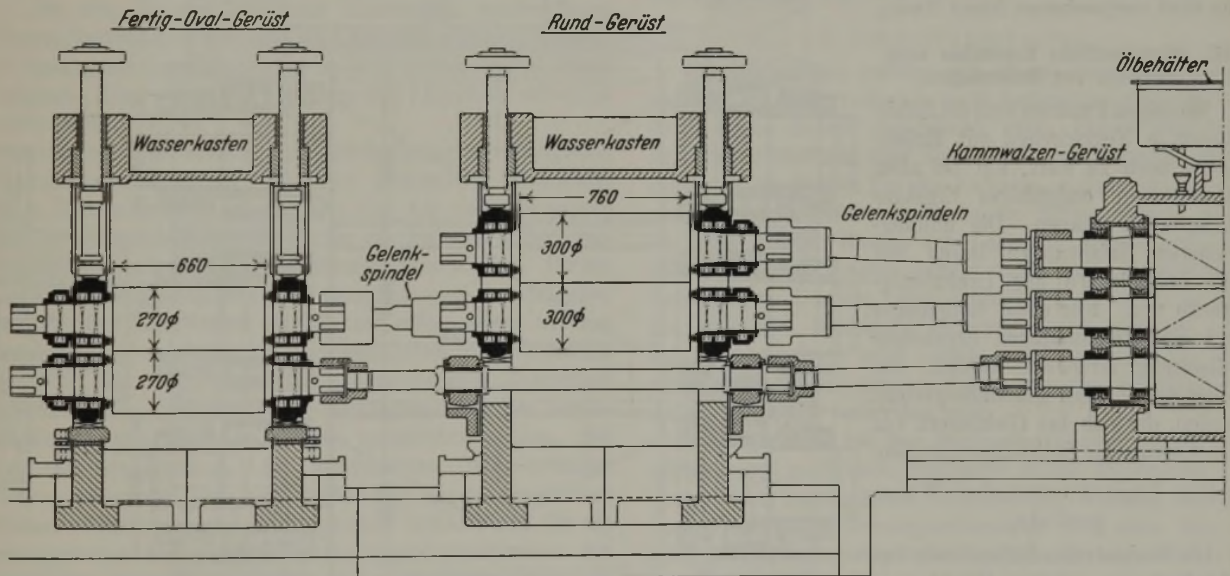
Walzgerüste mit Rollenlagern in der Fertigstrecke.
